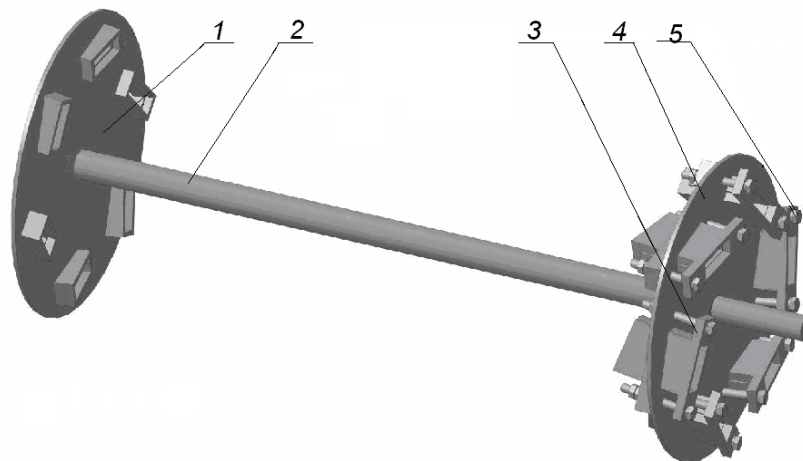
Конструкция многоместного приспособления для обработки детали в закрепленном состоянии:
